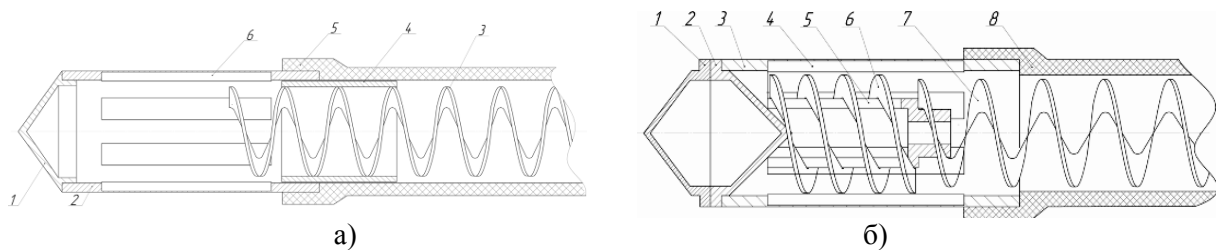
Конструкції навантажувально-захисних насадок ГК
